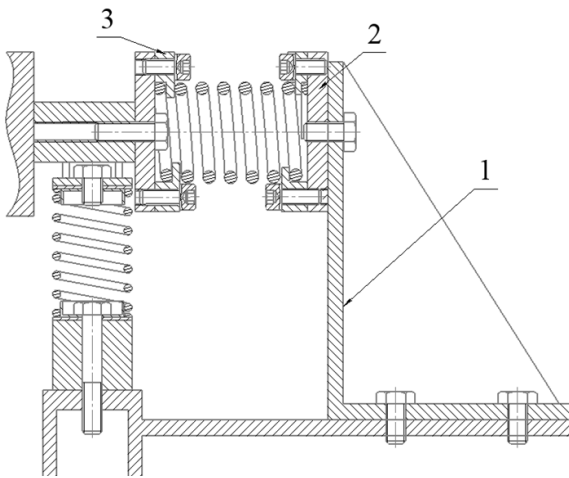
Сборочный чертеж узла крепления пружины в разрезе.
